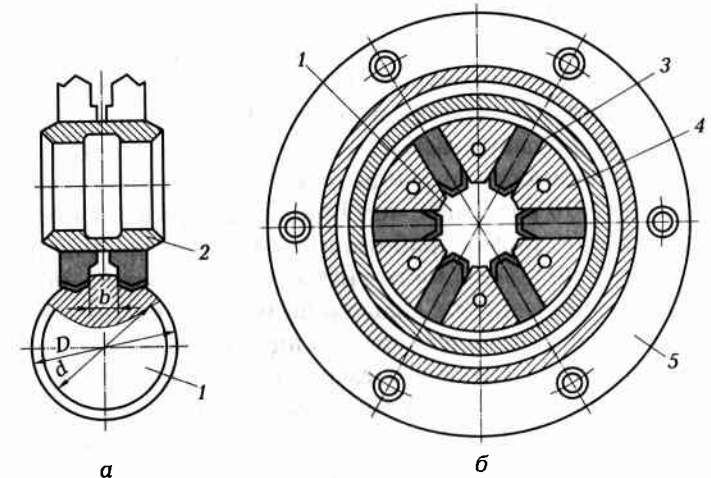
Схема нарезания шлицов на валах фасонными фрезами (а) и резцовая головка шлицестрогального станка (б):
